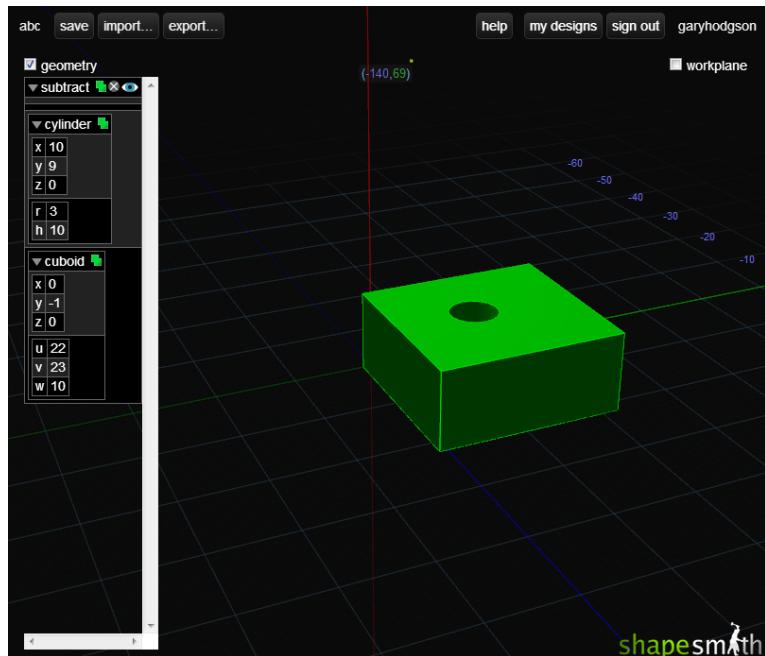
Outil de CAO en ligne Shapesmith.
